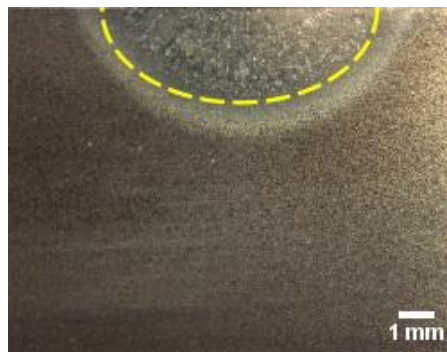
Seção transversal de cordão de solda TIG. Fonte: Autor.
